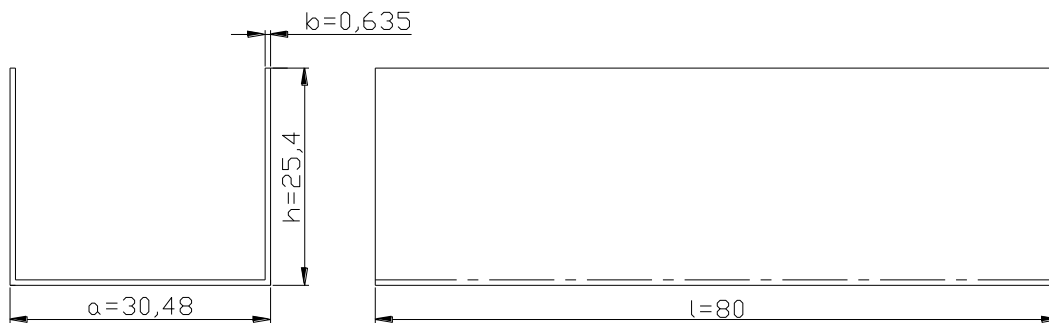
Dimensiones en cm del soporte del motoreductor. Fuente. Propia.
